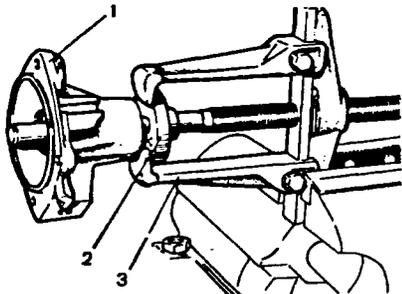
Снятие ступицы шкива: 1 - крышка корпуса насоса; 2 - ступица шкива; 3 - съемник
